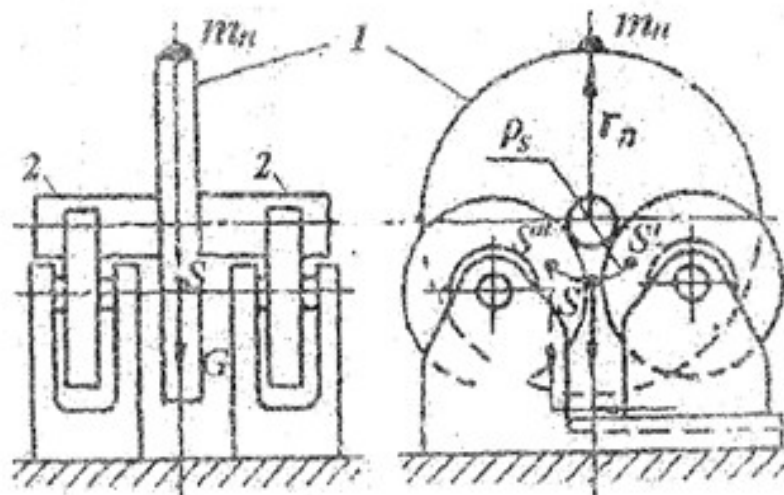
Станок с упорами в виде подшипников для статической балансировки.
